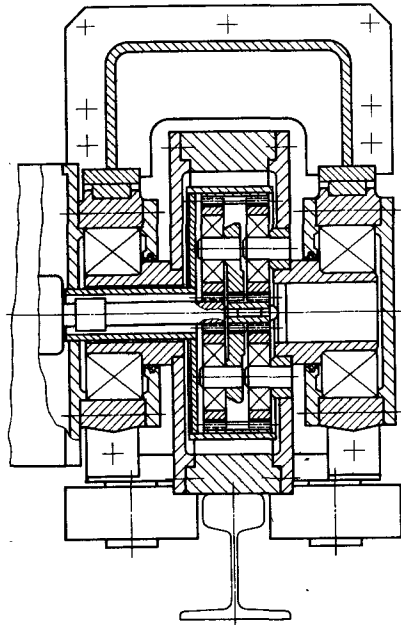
Ходовое колесо с встроенным планетарным редуктором
